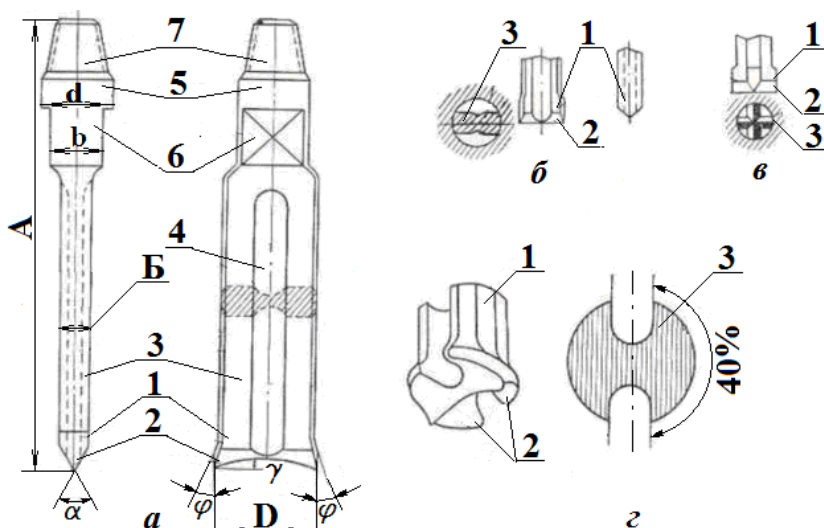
Схема долота для ударного буріння (а) та форми робочих насадок доліт: б – зубило; в – хрестова; з – копитоподібна; 1 – голівка; 2 – лезо; 3 – поверхня дроблення
